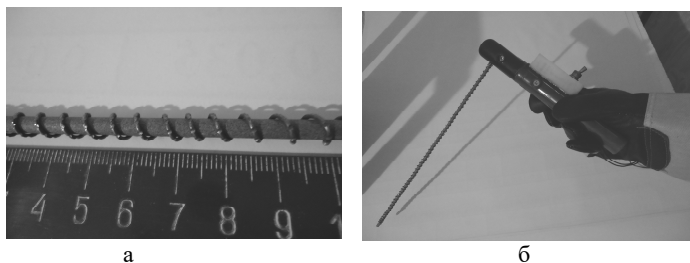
Технология ручной дуговой сварки с комплексным воздействием на жидкий металл сварочной ванны: а- спиральное крепление макрохолодильника к электроду; б- крепление эксцентрикового вибратора к электрододержателю
